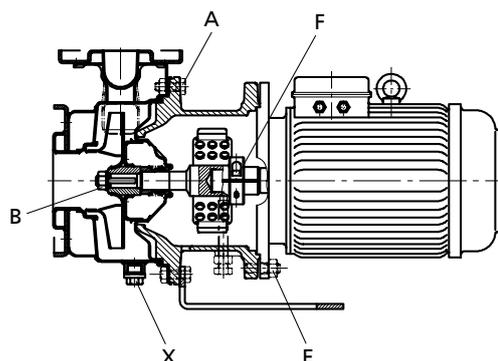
Ubicación de los tornillos para Etachrom B 050-025-125.1, 050-025-125, 050-025-160, 050-025-200, 050-032-125.1, 050-032-125, 050-032-160, 050-032-200, 065-040-125, 065-040-160, 065-040-200, 065-050-125, 065-050-160
